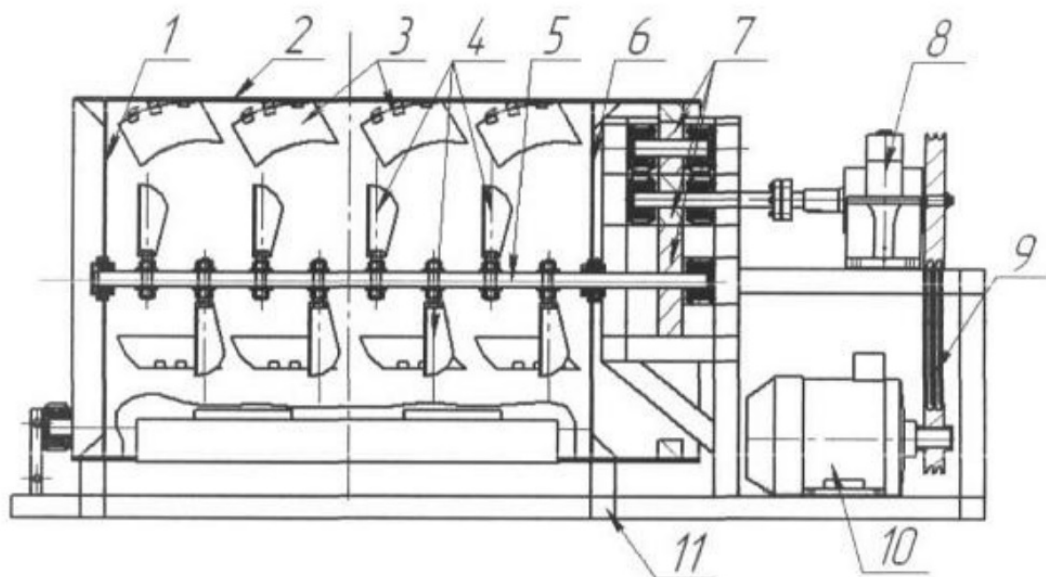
Змішувач гравітаційно-примусової дії: 1 – ліва торцева стінка; 2 – барабан; 3, 4 – лопаті; 5 – вал; 6 – права торцева стінка; 7 – зубчаста передача; 8 – редуктор; 9 – клинопасова передача; 10 – двигун; 11 – рама
